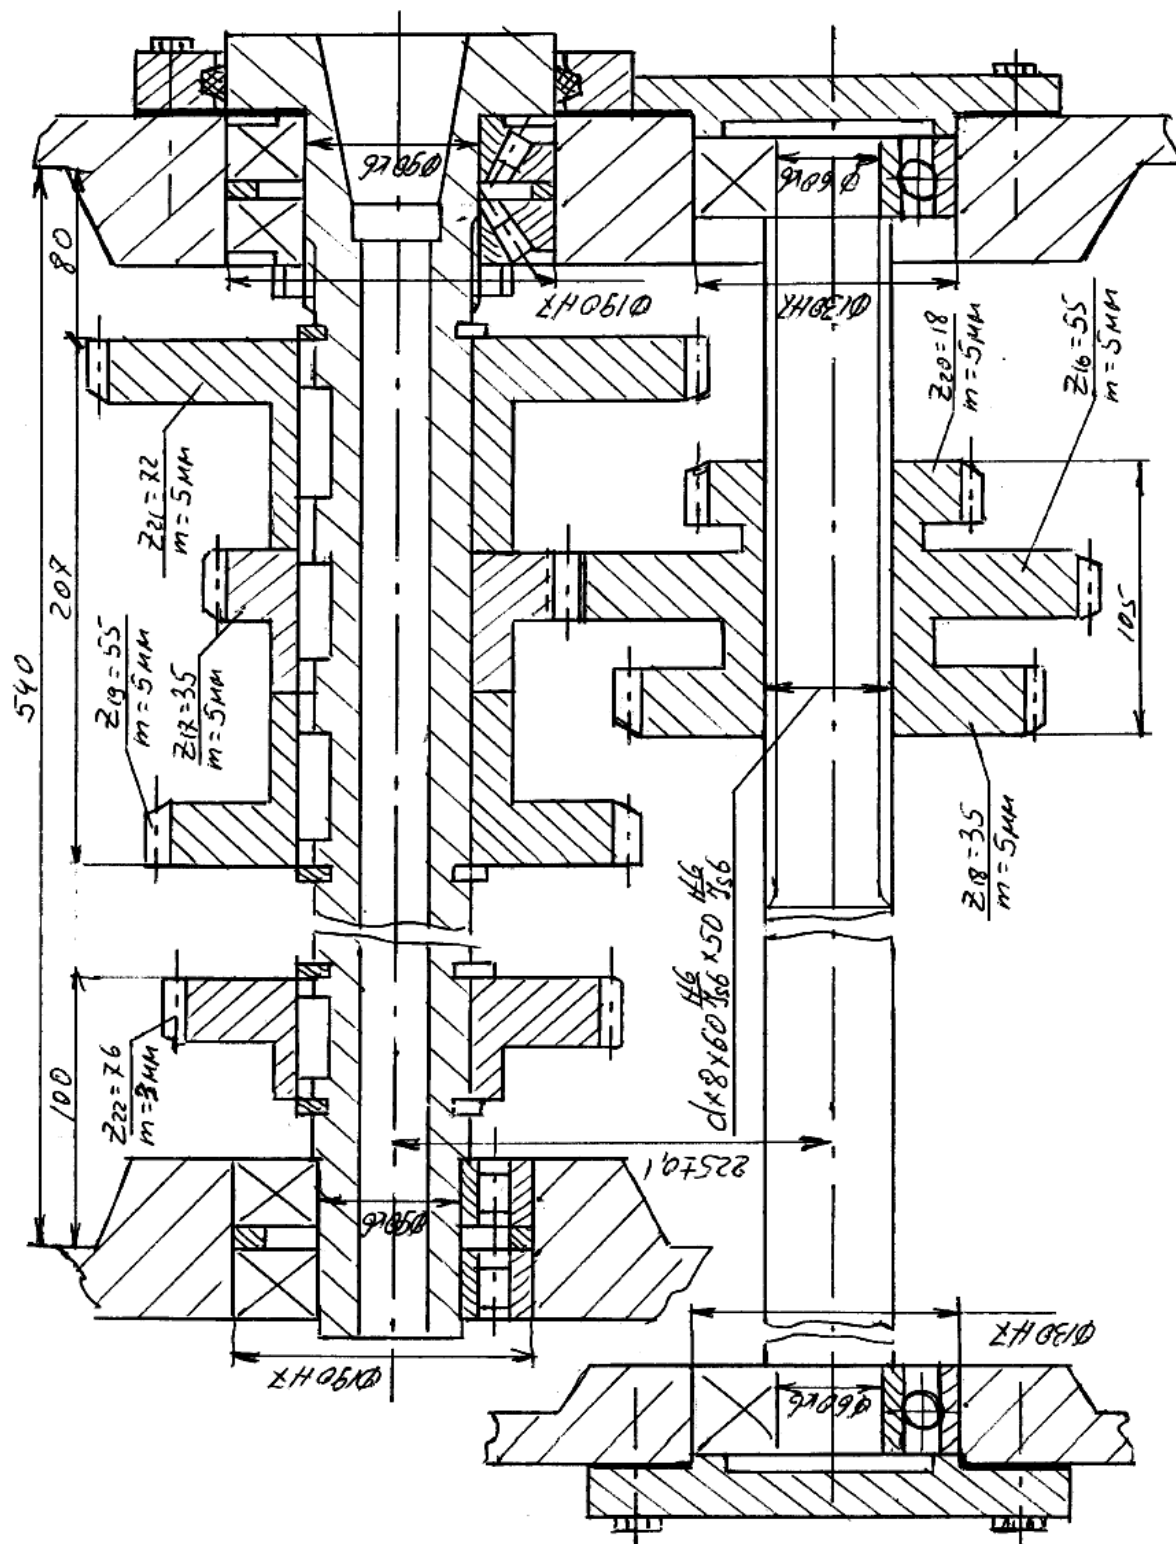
Сборочный чертеж наиболее нагруженной группы передач
